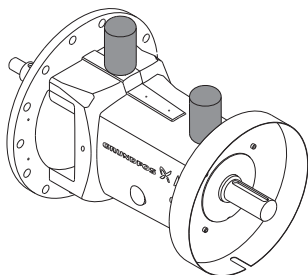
Корпус подшипников с автоматическими масленками для консистентной смазки
